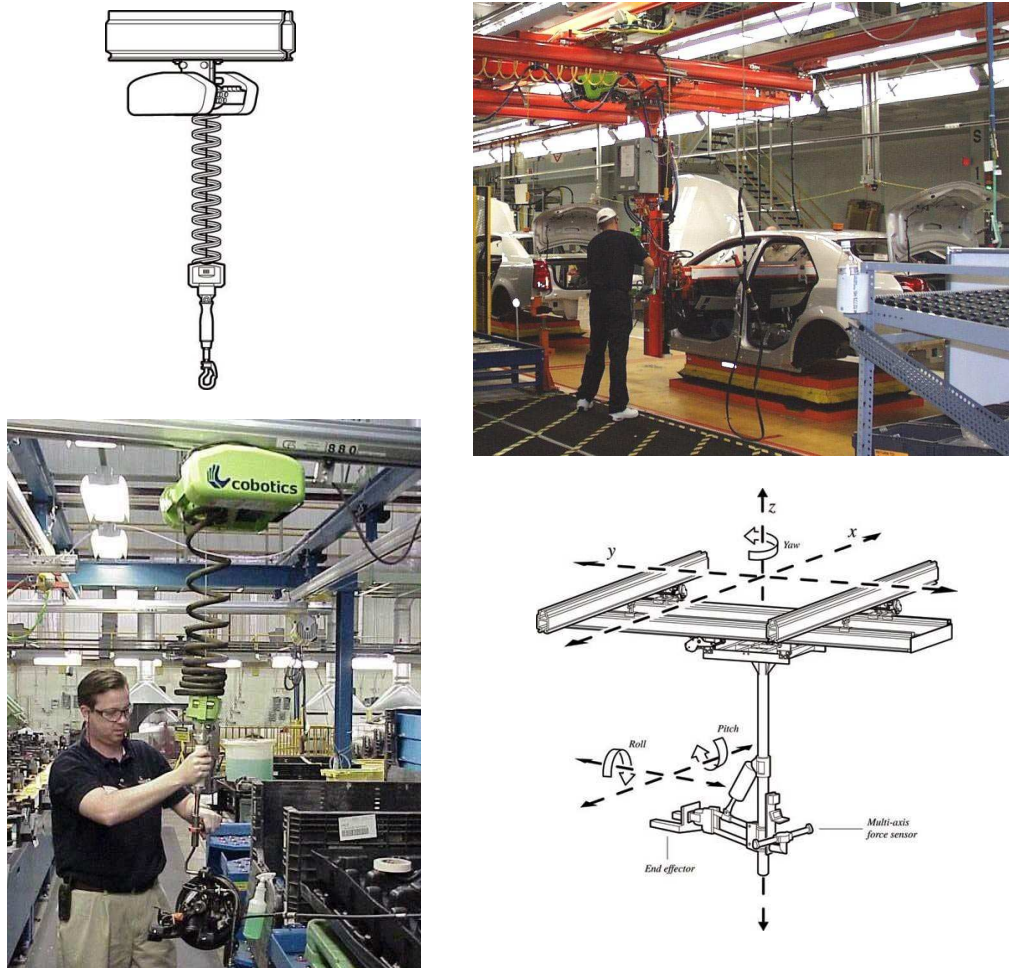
Robots d’assistances au montage actuellement disponibles pour l’industrie (photos de Stanley Assembly Technologies).
